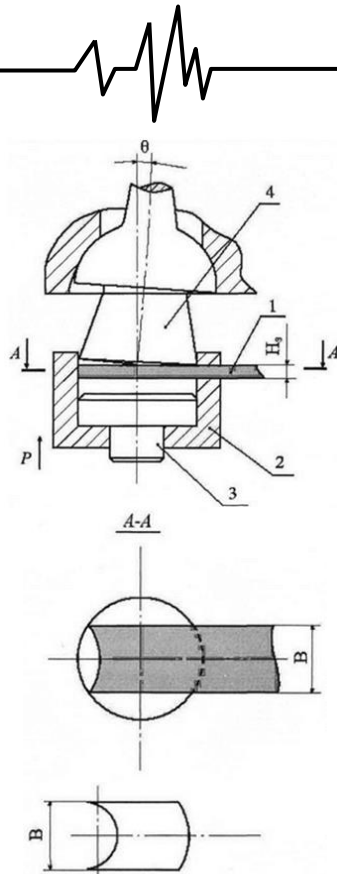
Схема комбінованого процесу рубки і штампування обкочуванням плоских заготовок для виготовлення деталей (переріз А-А відрубана частина смугової заготовки):
